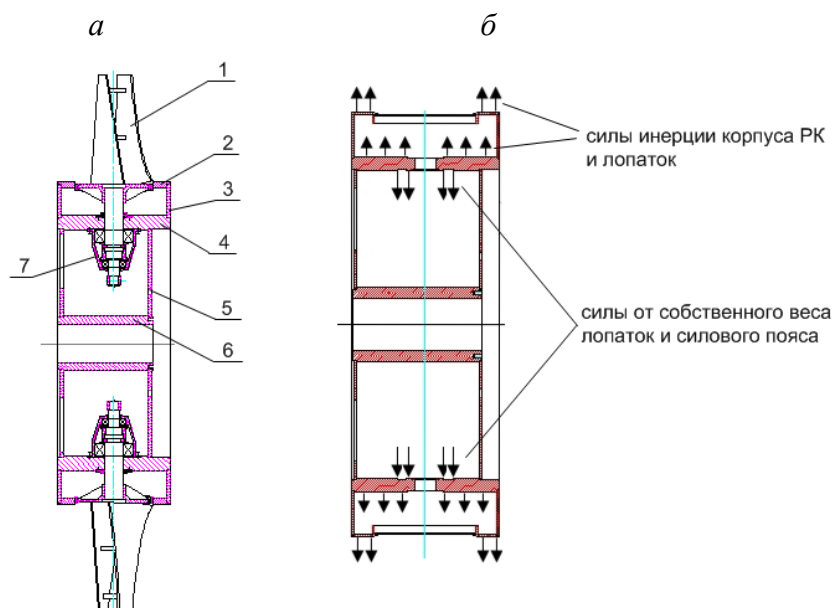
Конструктивная схема рабочего колеса (а) и нагрузок, действующих на корпус РК вентилятора ВО-36К (б): 1 – лопаточный узел; 2 – обечайка; 3 – опорный диск; 4 – силовой пояс; 5 – несущий диск; 6 – ступица; 7 – стакан
